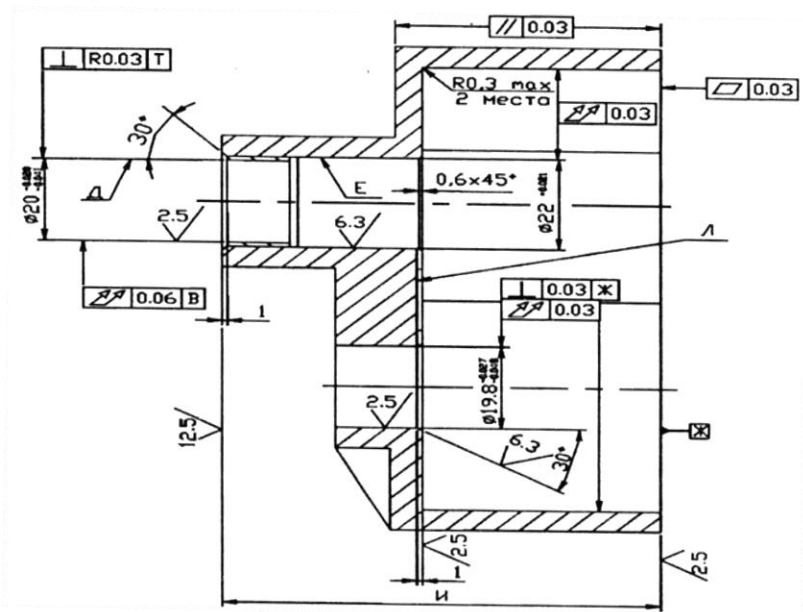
Корпус масляного насоса двигателя КАМАЗ-740
